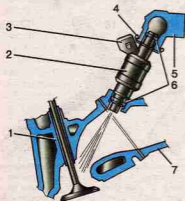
Установка топливной форсунки: 1 – впускной клапан; 2 – форсунка; 3 – штифтовый разъем; 4 – фиксатор; 5 – рампа форсунок; 6 – уплотнительные кольца; 7 – впускная труба
